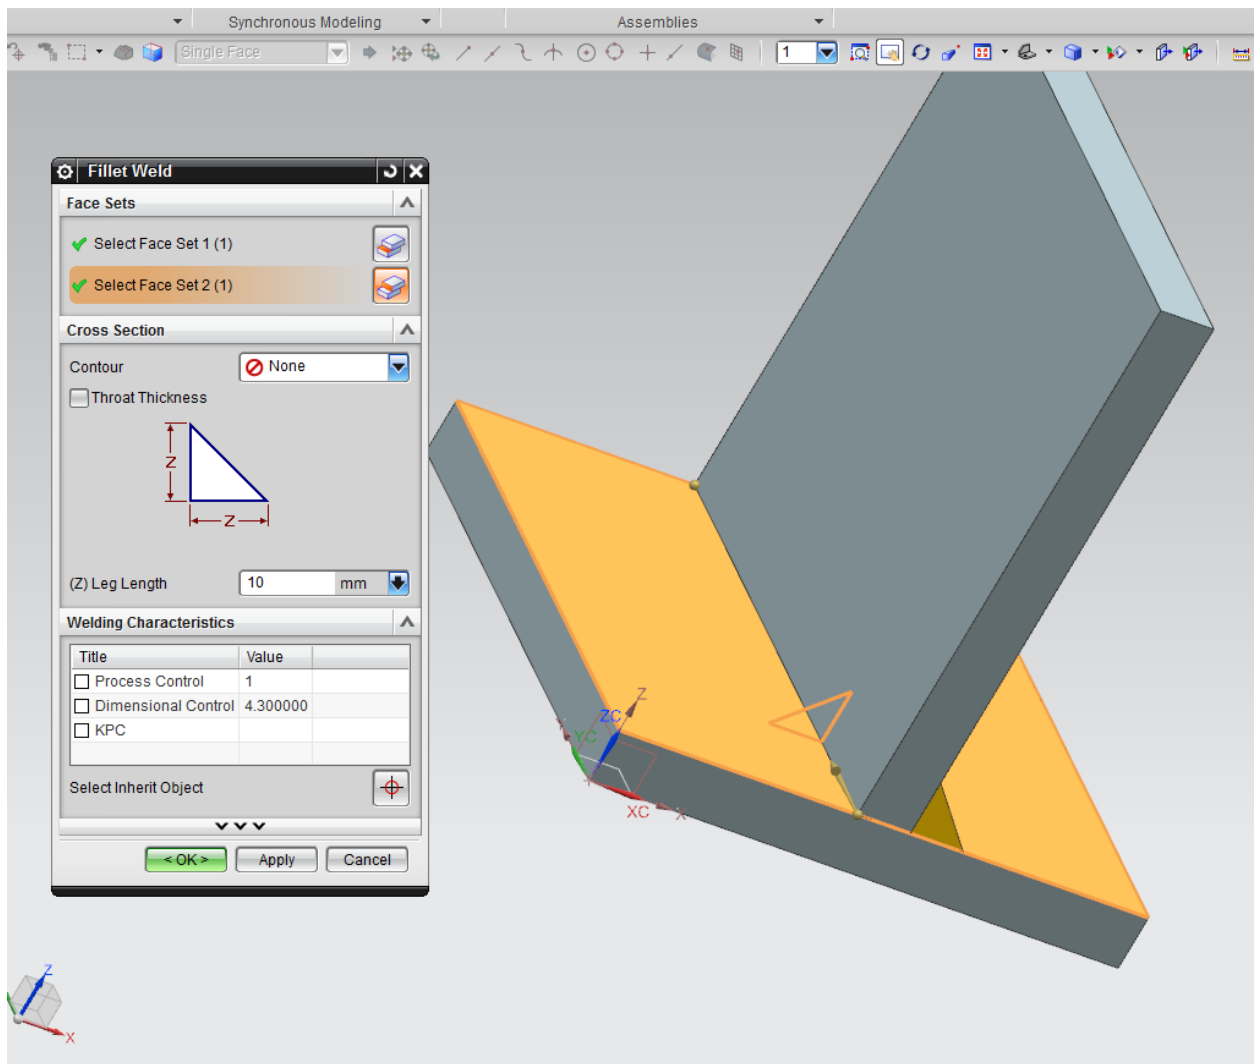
Подготовленная к выполнению сварного соединения сборка
